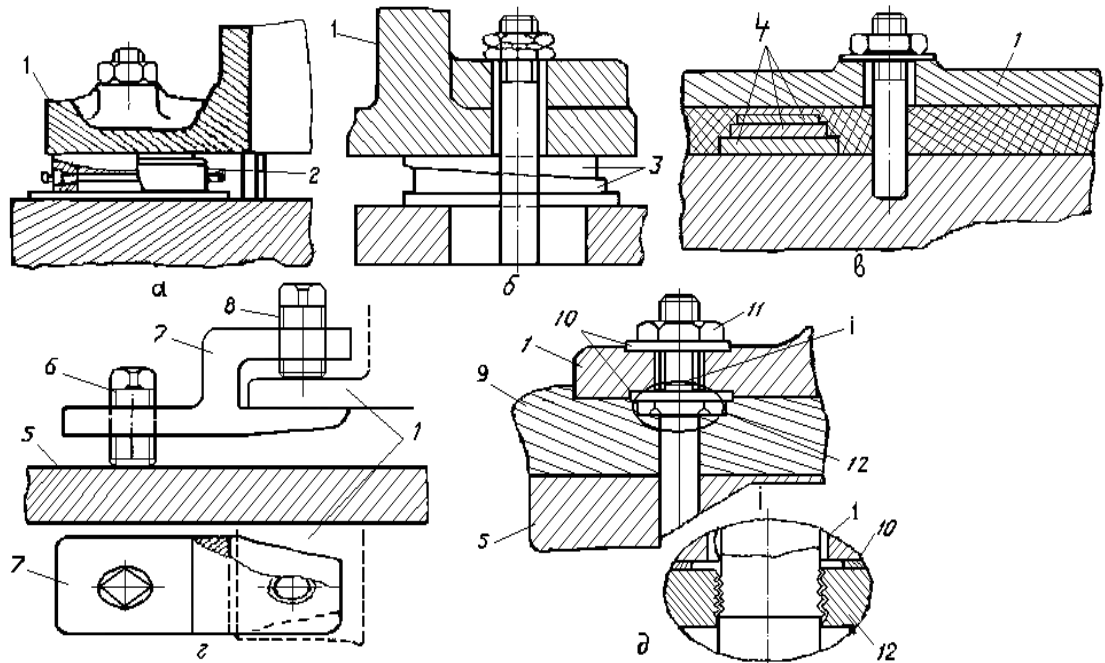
Схема кріплення обладнання на фундаментах і підставах:
